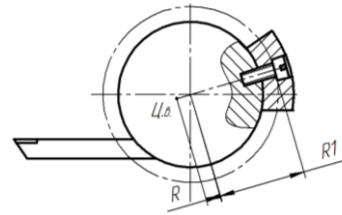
Кресленник схеми для визначення маси противаги за її конструктивними параметрами
